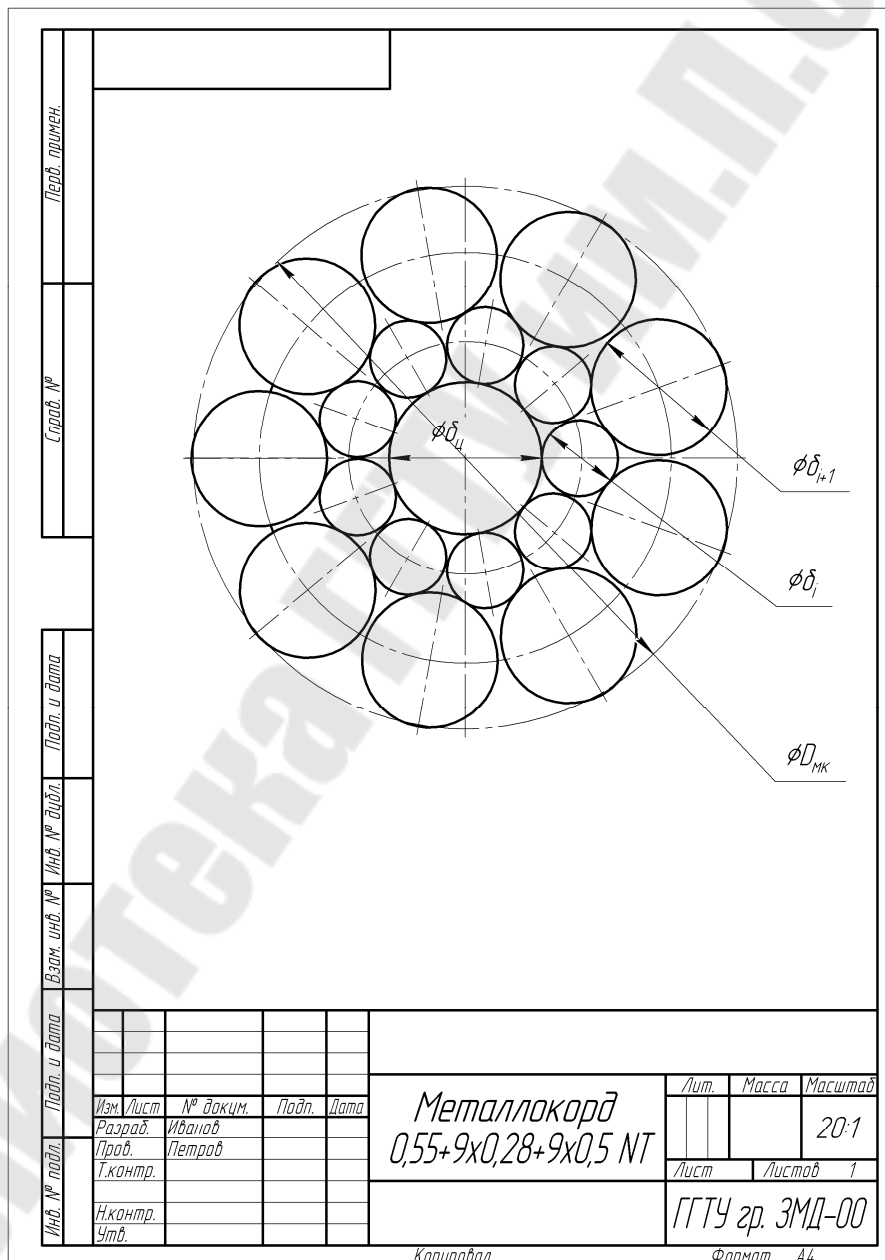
Пример оформления чертежа поперечного сечения металлокорда
